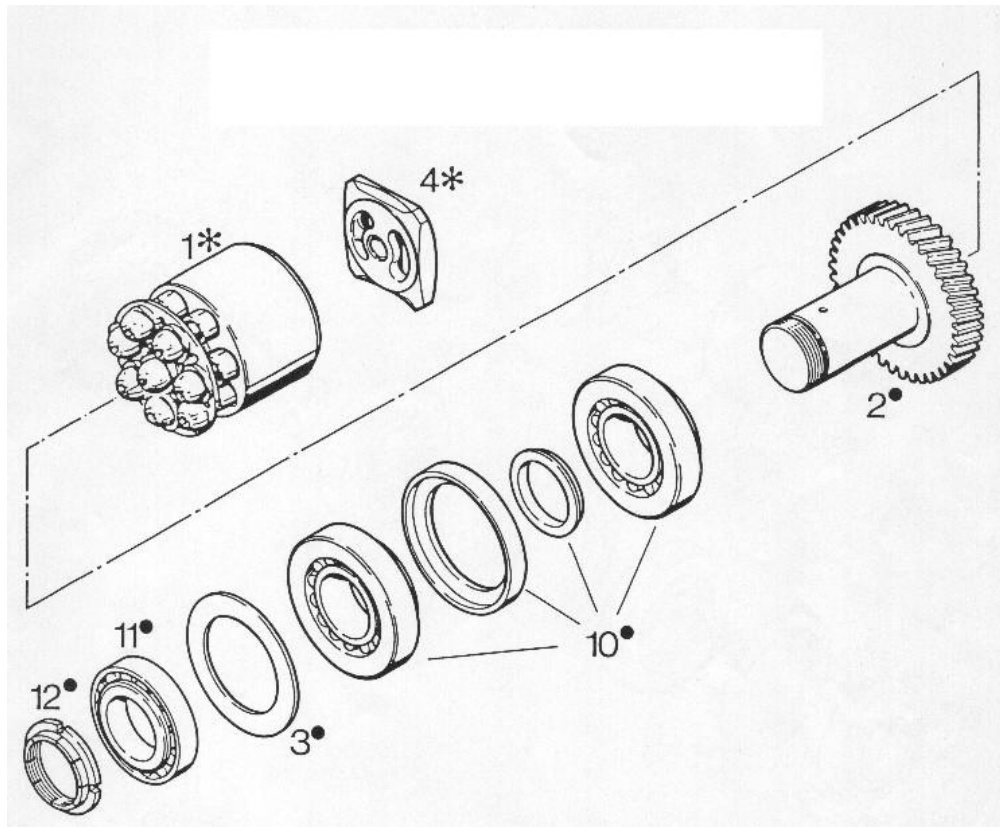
Vue éclatée de l'ensemble rotor hydrostatique1
